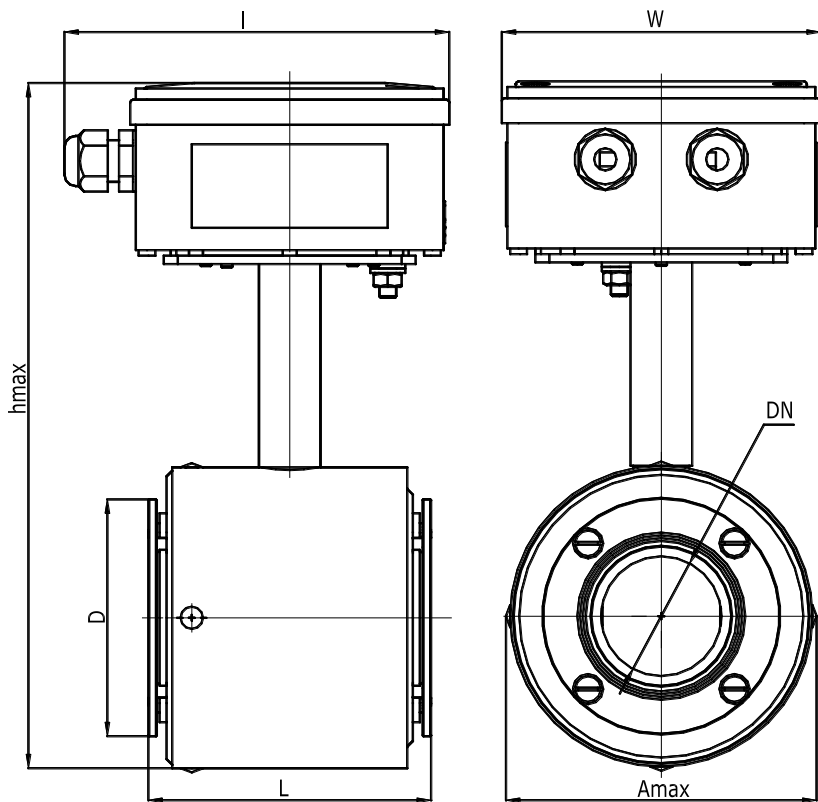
Габаритные и установочные размеры ПРПМ (ПРПП)
